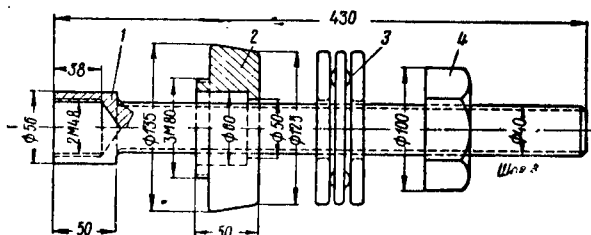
Приспособление для напрессовки якоря генератора тока управления:
